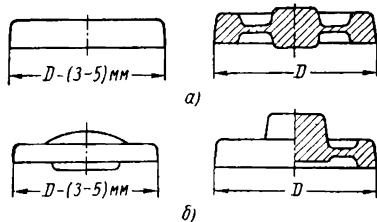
Варианты штамповки поковки, форма которых состоит из ступицы, диска и обода
